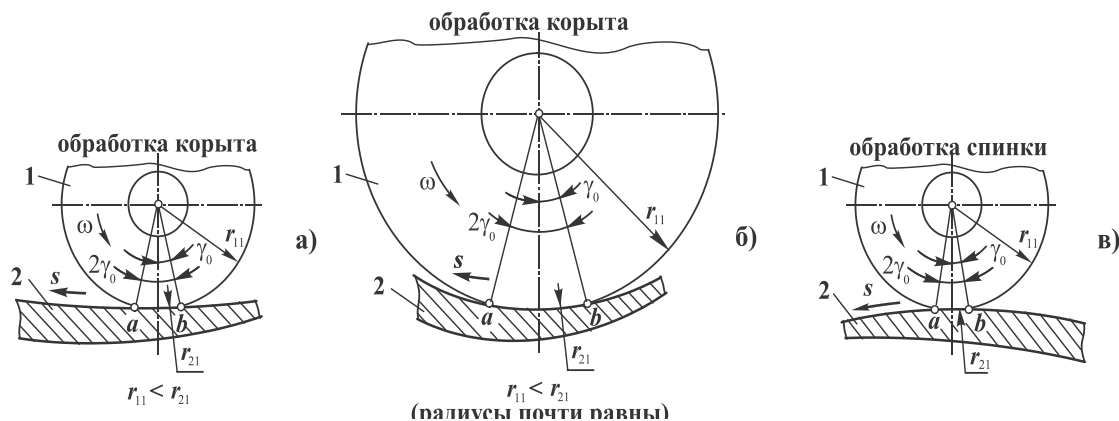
Схемы обработки поверхностей лопатки ГТД (вид сбоку):
